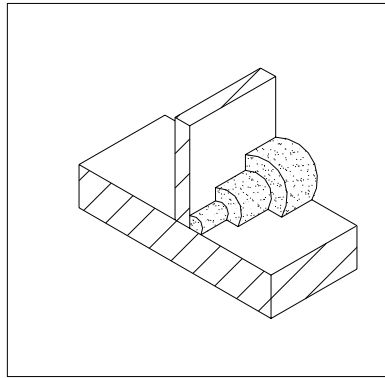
PASADAS EN SOLDADURA
